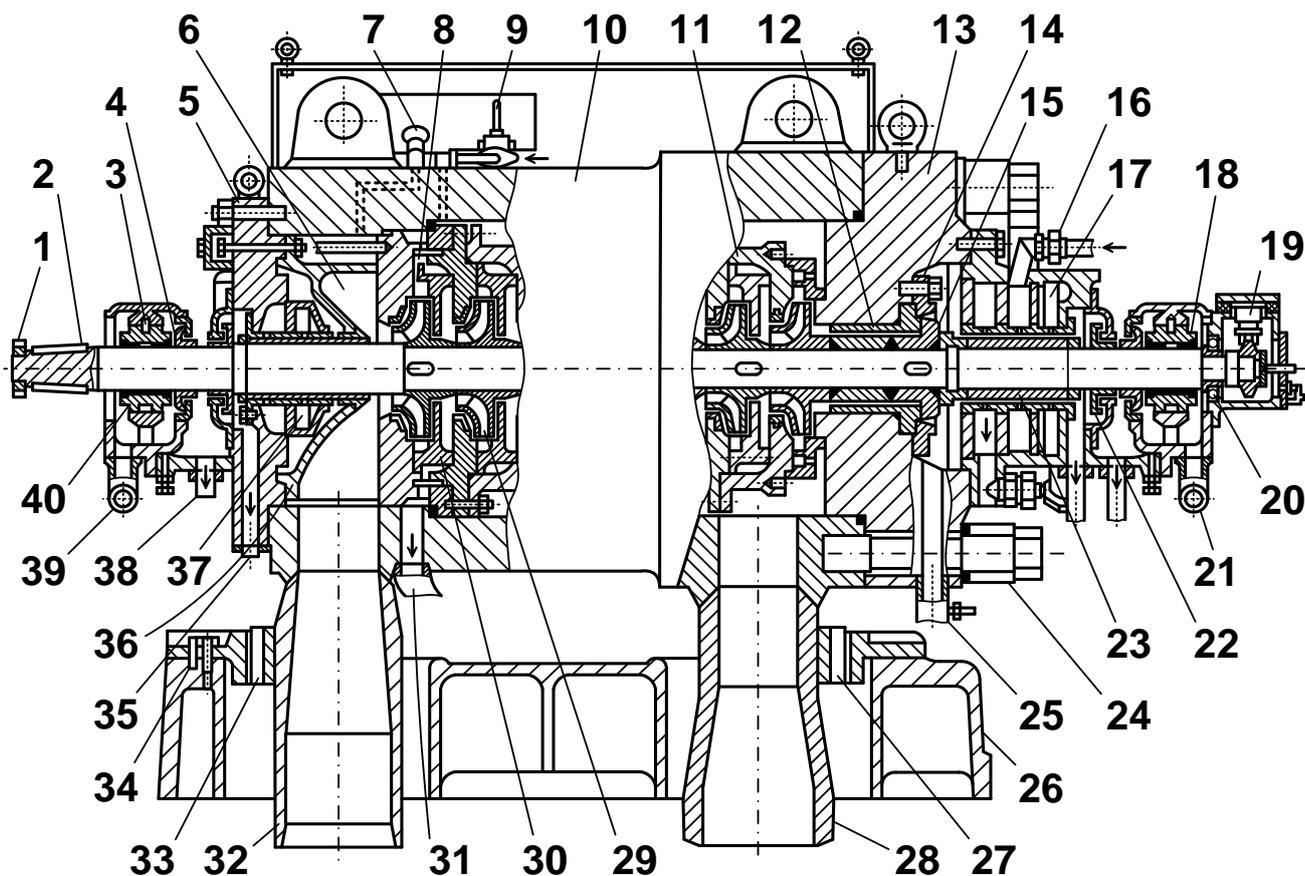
Пускорезервный питательный насос ПЭ-600-300
